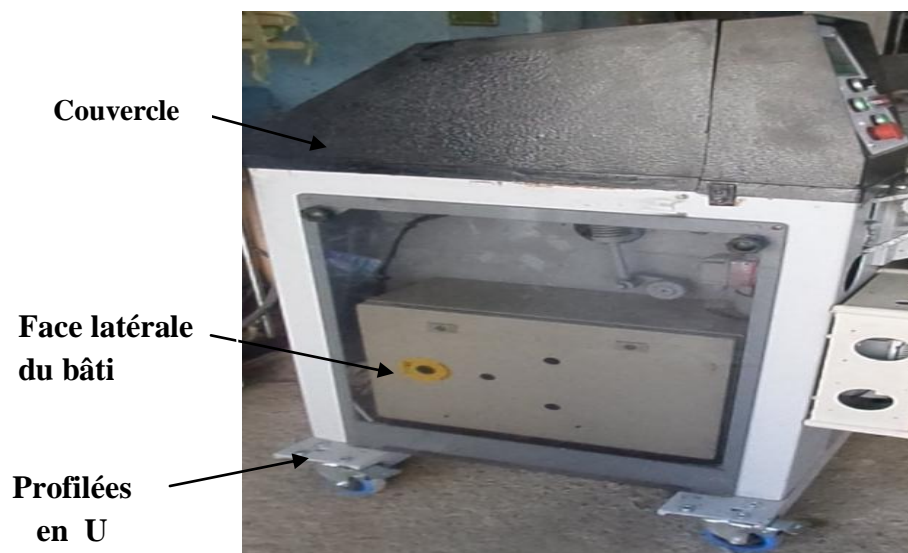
Ensemble des pièces vues du côté face latérale du bâti.
